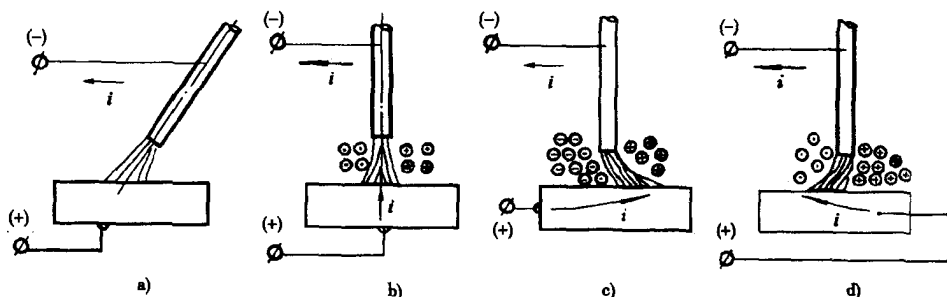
正常的焊接电弧和电弧的磁偏吹
